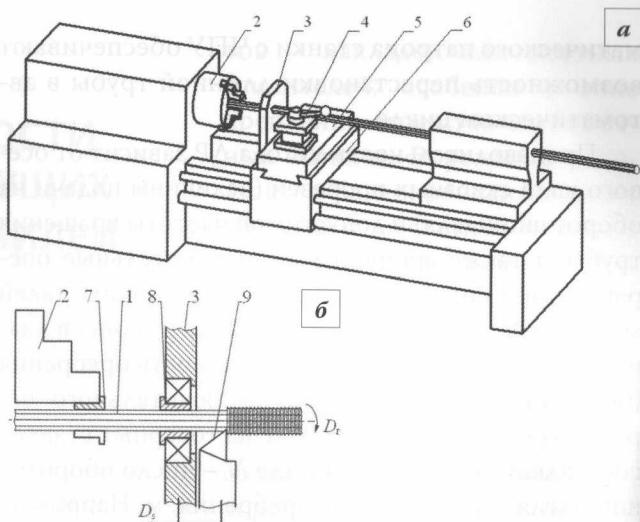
Получение сквозных щелей на токарном станке из продольно-гофрированной трубной заготовки: а – общая схема компоновки; б – схема обработки
